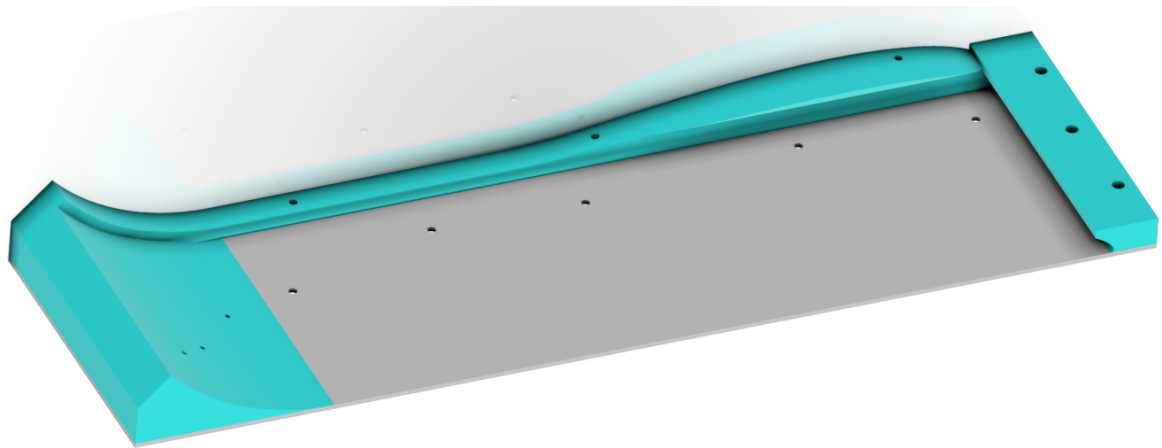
Sestava forem a lisovaného kompozitu horizontální zahnuté desky vozu FS.14
